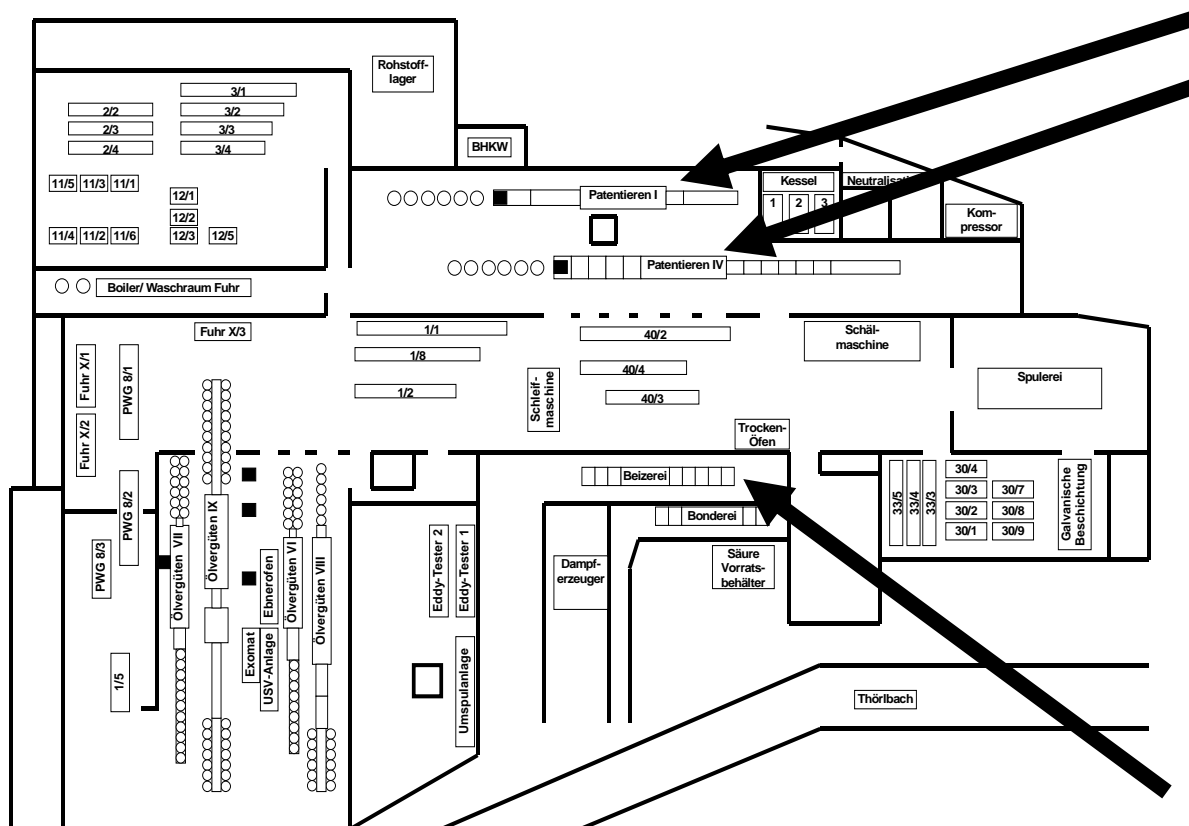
Lageplan der Komponenten, in denen derzeit Dampf eingesetzt wird.
